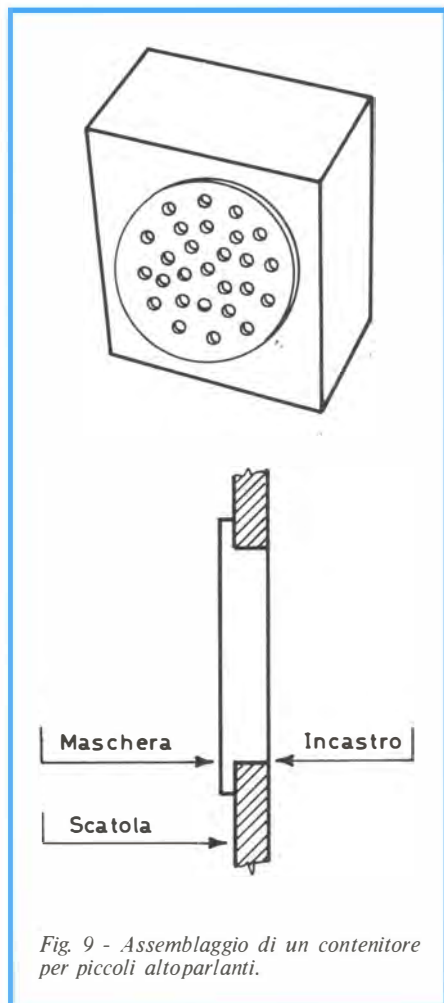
Assemblaggio di un contenitore per piccoli altoparlanti.
